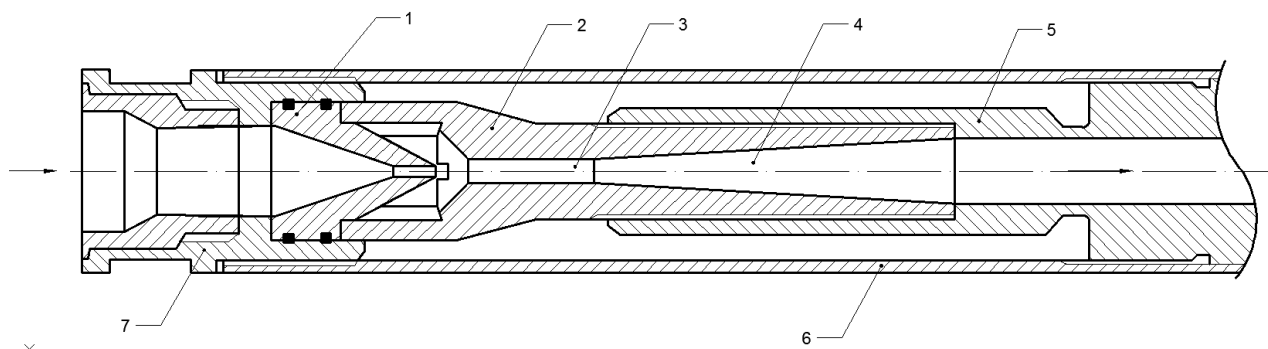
Конструкция скважинного струйного насоса для совместной работы с УЭЦН: 1 – высоконапорное сопло; 2 – корпус диффузора; 3 – камера смешения; 4 – диффузор; 5 – центрирующая муфта; 6 – корпус; 7 – муфта сопла
